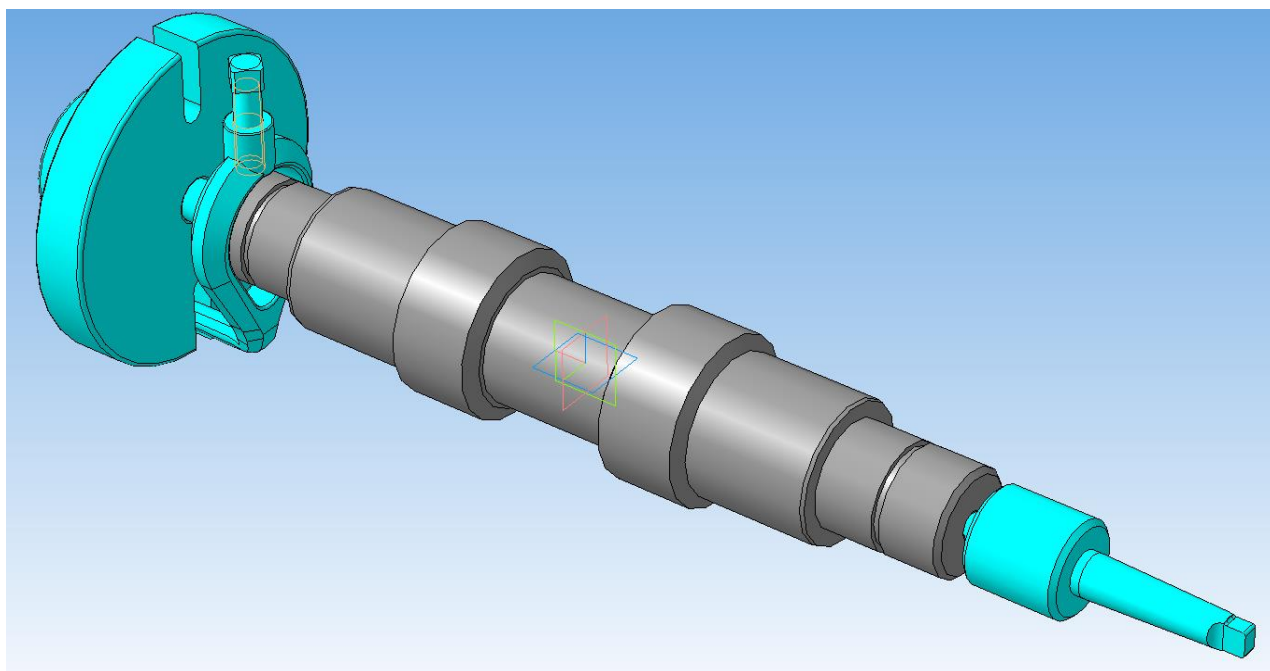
Розроблений верстатний пристрій з установленою деталлю
